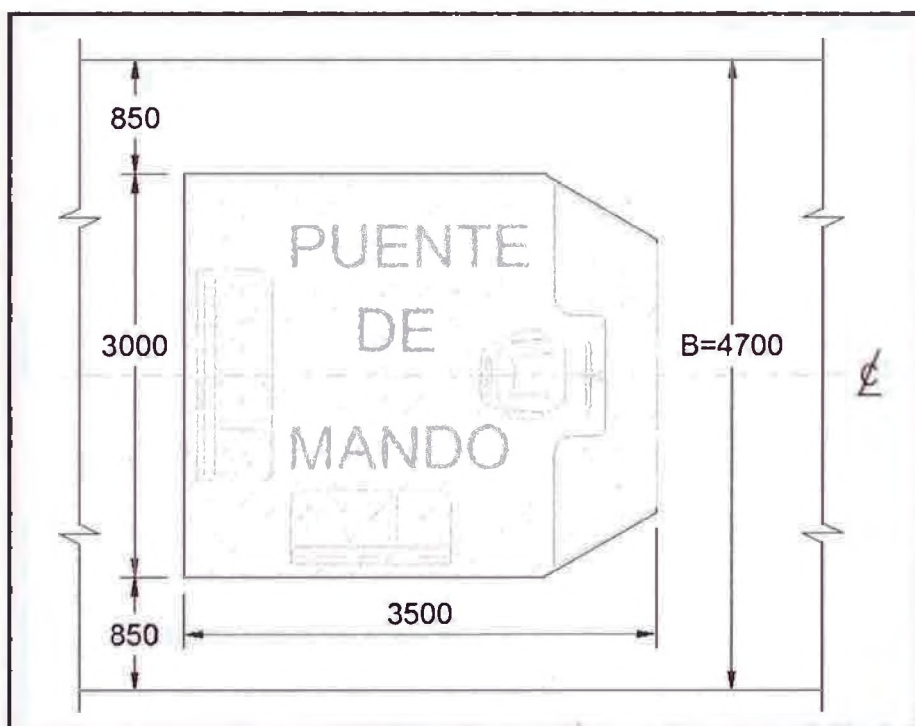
Croquis del Puente de Mando (vista de planta).
